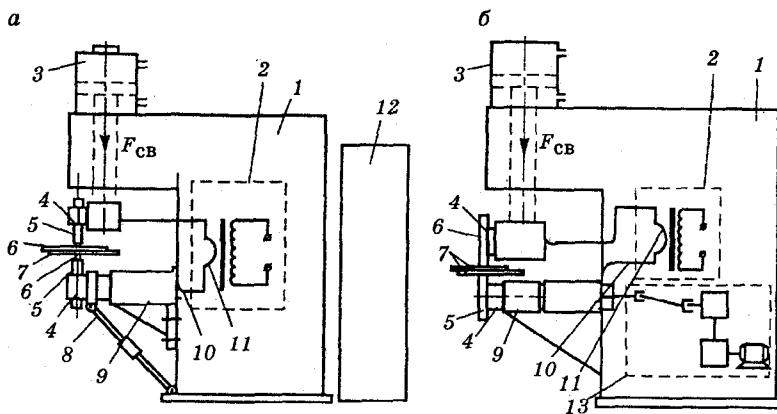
Схемы машин для точечной (а) и шовной (б) сварки: 1 — корпус; 2 — сварочный трансформатор; 3 — привод сжатия; 4 — консоли; 5 — электродержатели; 6 — электроды; 7 — детали; 8 — подкос; 9 — кронштейн (держатель); 10 — гибкие шины; 11 — вторичный виток трансформатора; 12 — шкаф управления; 13 — привод вращения электродов (роликов)
